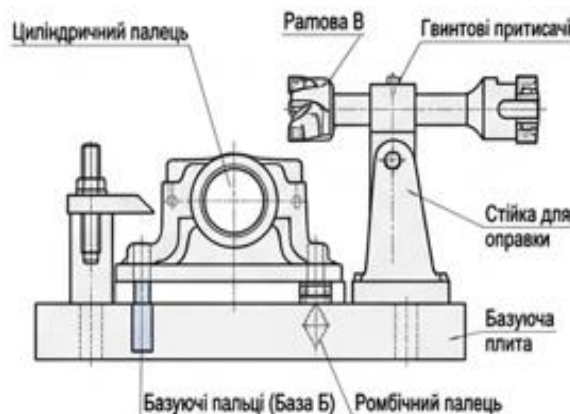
Розточний стенд з базуючими пальцями
